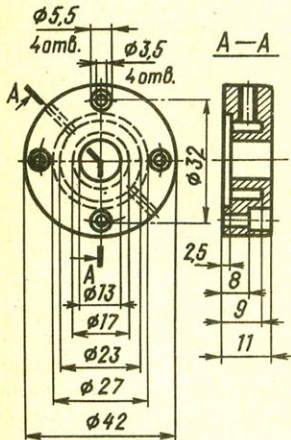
Охлаждаемая головка цилиндра двигателя (Д16Т).
